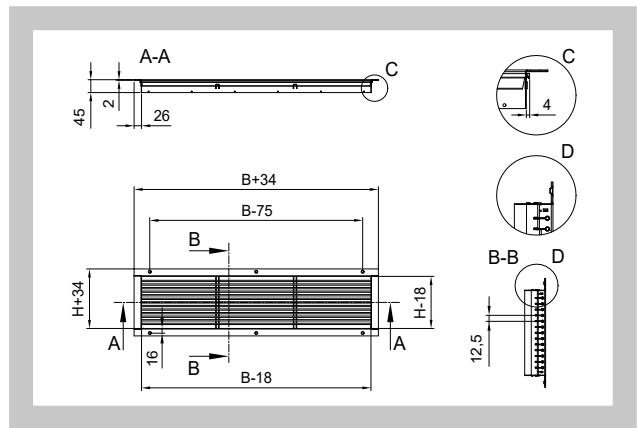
Feste Lamellen - Lamellenabstand 20 mm
